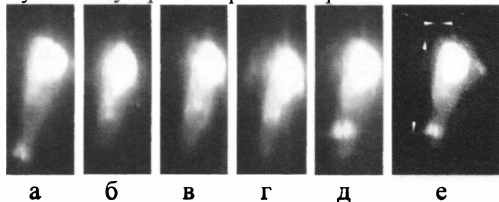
Механизм переноса расплавленного металла из зоны каверны в сварочную ванну при лазерной сварке.
